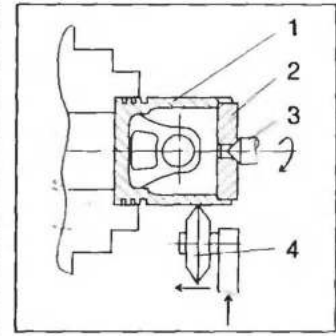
Установка поршня в токарном станке при накатке юбки:
